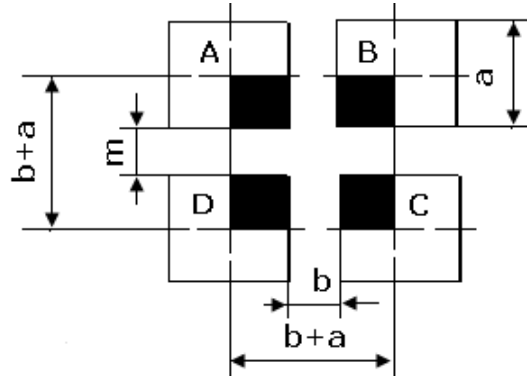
Dikdörtgen delikli eleklerde boyutlar
